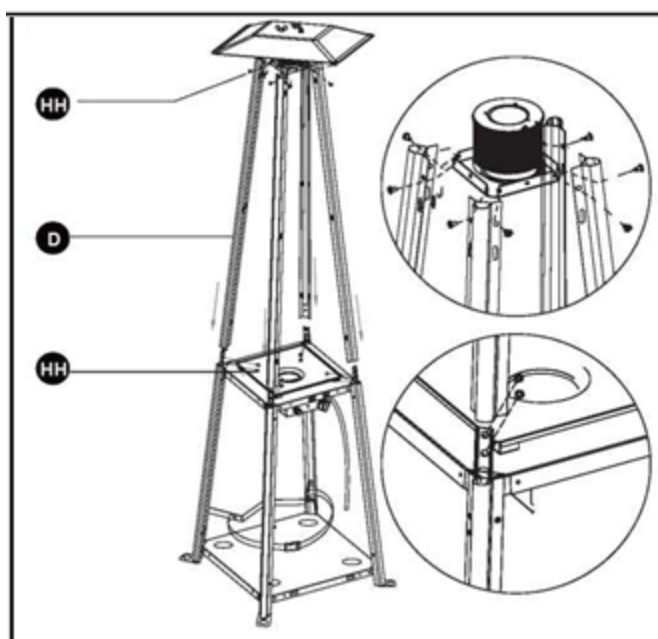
Сборка верхней, нижней опоры и установка дожигателя.
